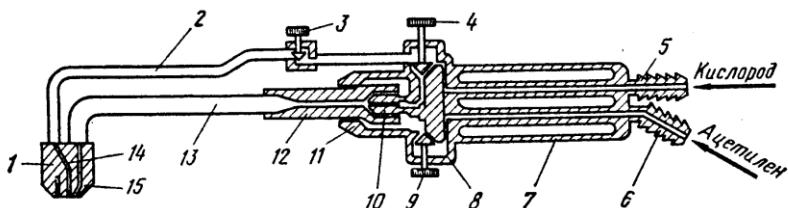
Схема устройства универсального ацетилено-кислородного резака: 1 – головка; 2 – трубка режущего кислорода; 3, 4, 9 – вентили; 5, 6 – ниппели для шлангов; 7 – рукоятка; 8 – корпус резака; 10 – инжектор; 11 – накидная гайка; 12 – смесительная камера; 13 – наконечник; 14 – внутренний мундштук; 15 – наружный мундштук
